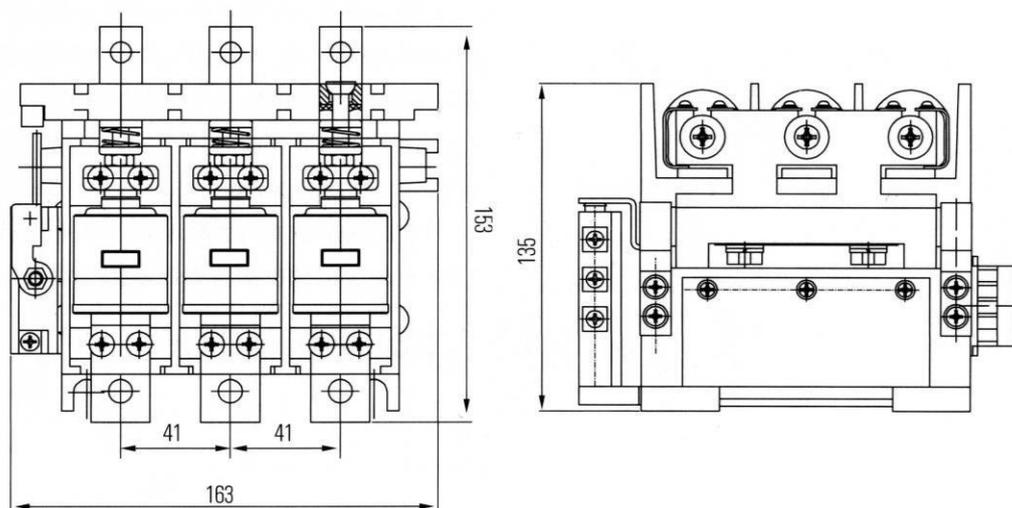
Габаритные размеры КВТ-1,14-80/125/160
